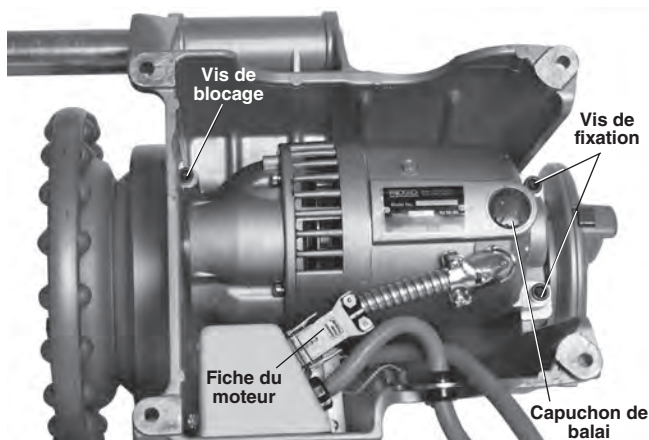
Dépose du carter inférieur du moteur pour le remplacement des balais
